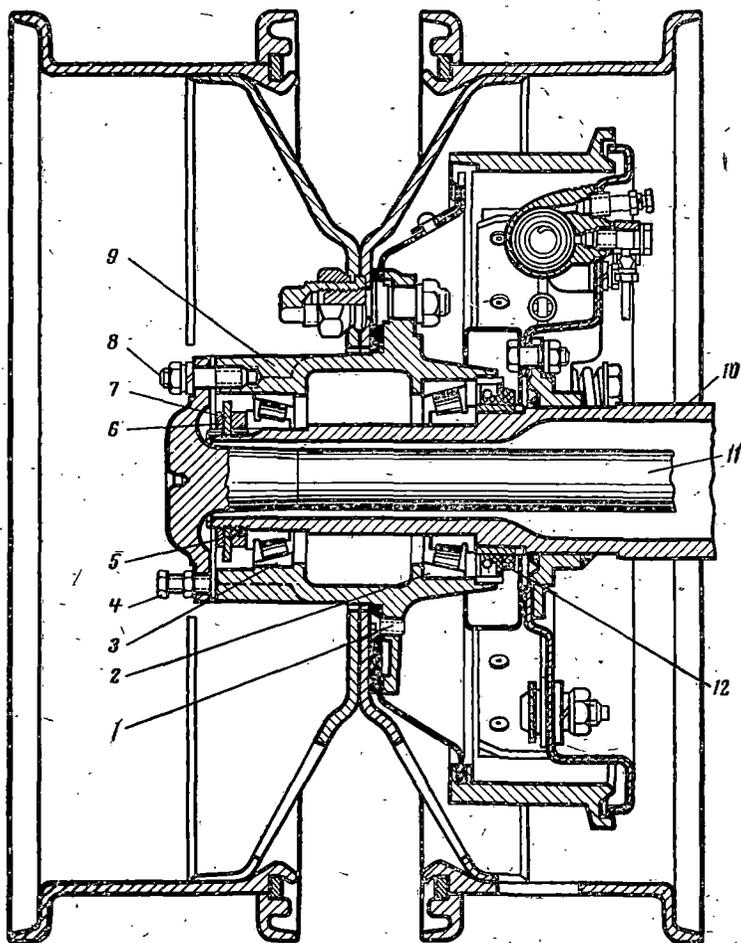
Крепление ступицы заднего колеса автомобилей ГАЗ-51А, ГАЗ-53А:
